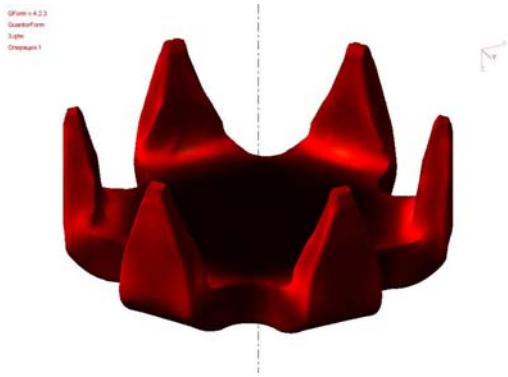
Поковка, изготовленная холодной объёмной штамповкой с последующей гибкой
